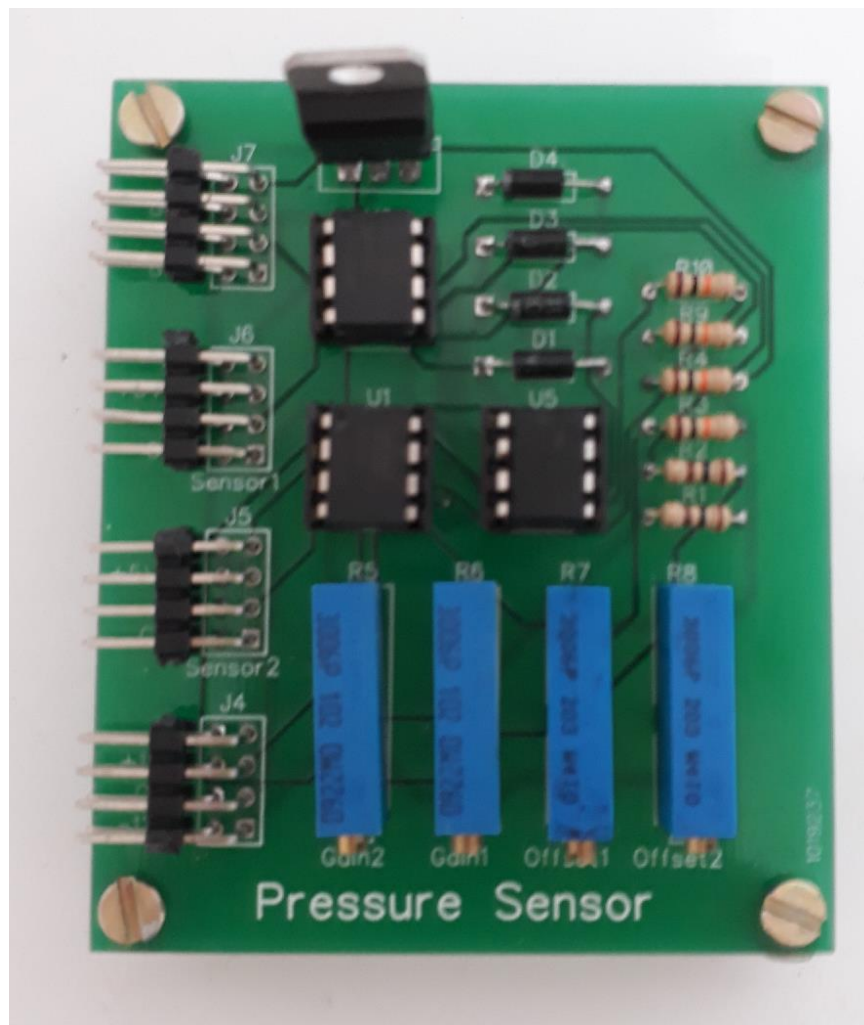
Circuito ceifador para o sensor de pressão soldados a PCB dupla face.
